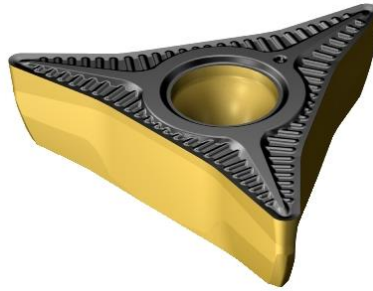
Plaquita para torneado CoroTurn Prime CP-A1104-L5-4325
